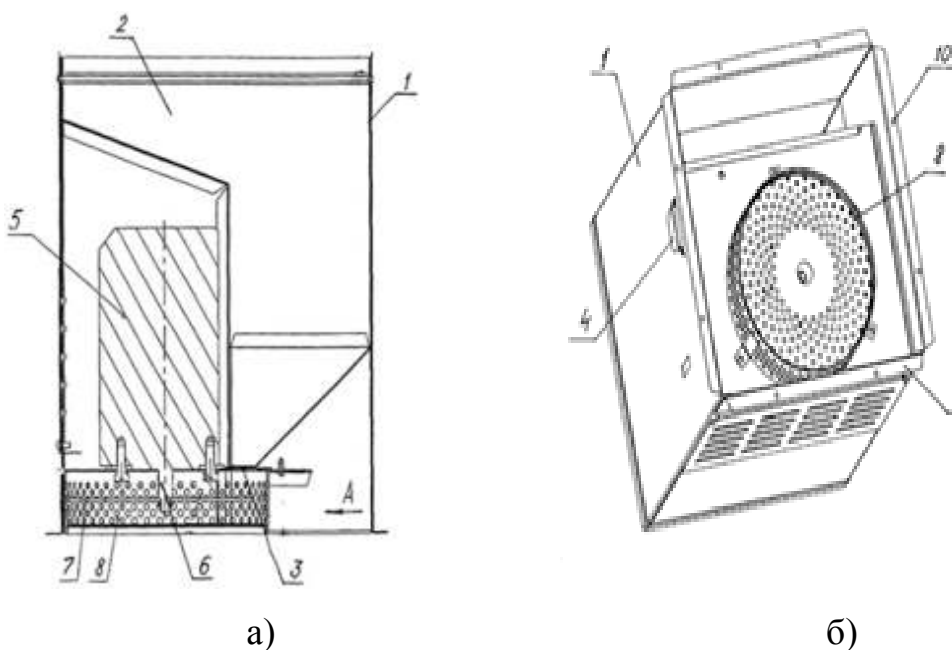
Устройство для измельчения зерна (патент РФ 116 790)
